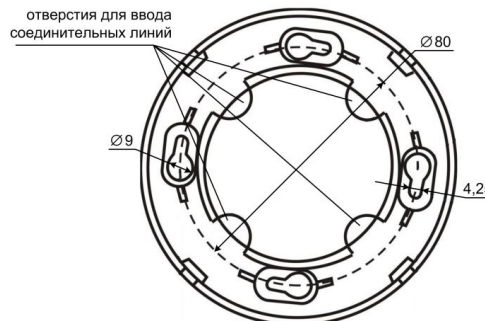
Расположение отверстий для крепления базы извещателя. Присоединительные размеры
